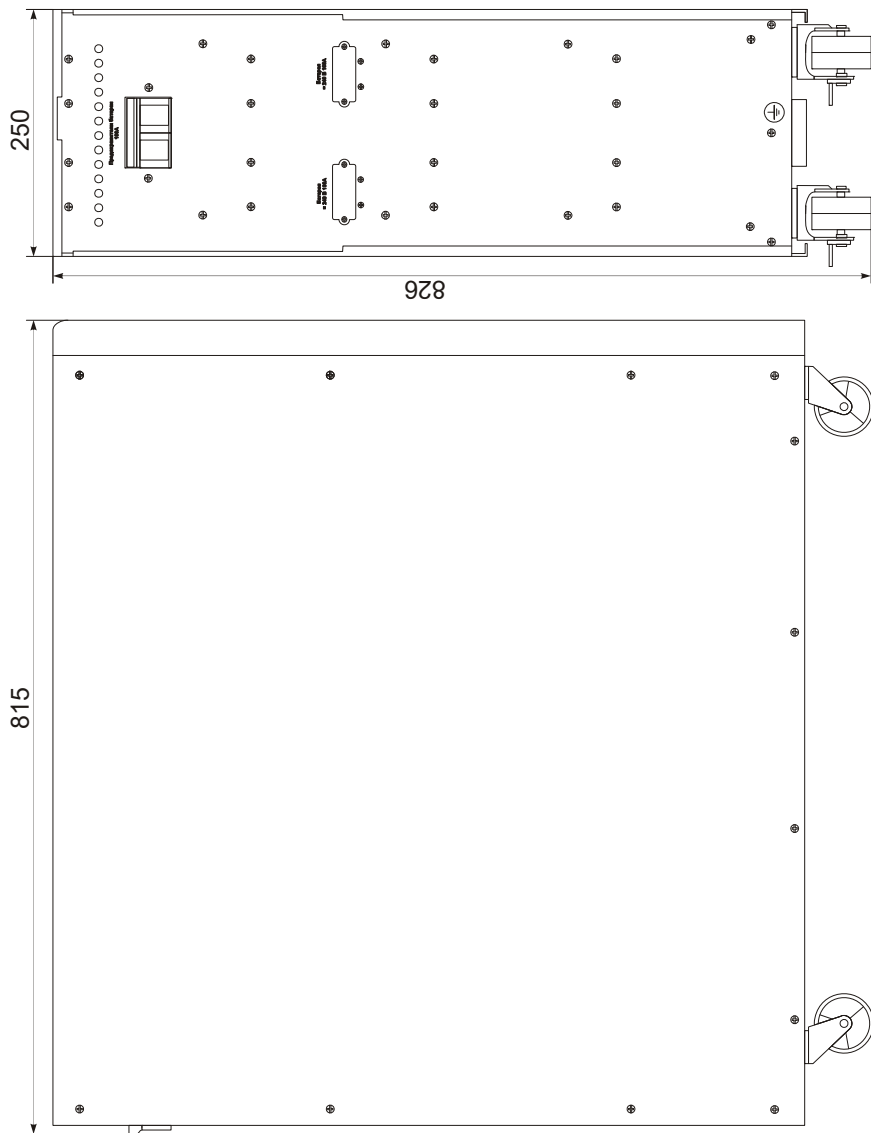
Габаритные и установочные размеры БМ ВР 240-36-100А
